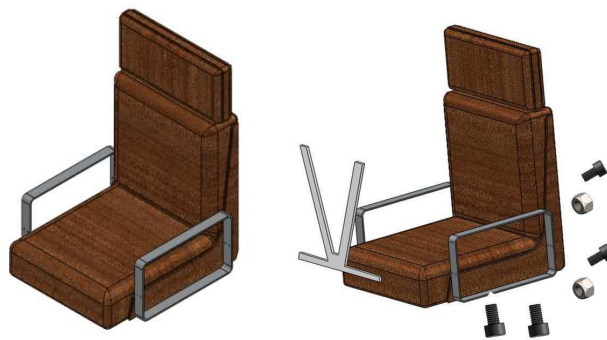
Conjunto cadeira, nas vistas isométrica e explodida.
